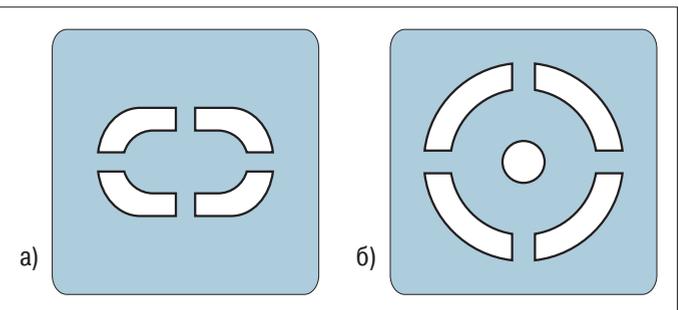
Подсоединение: а – планарной площадки к полигону, б – вывода к плану питания
